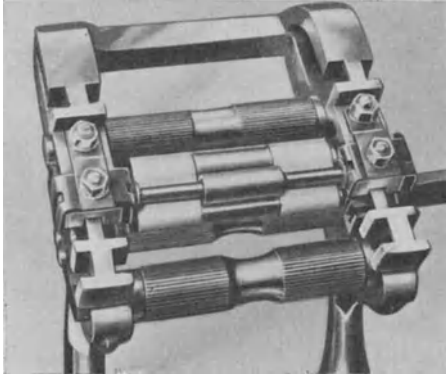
Walzenstreckwerk für Hochverzug, System Vanni.
